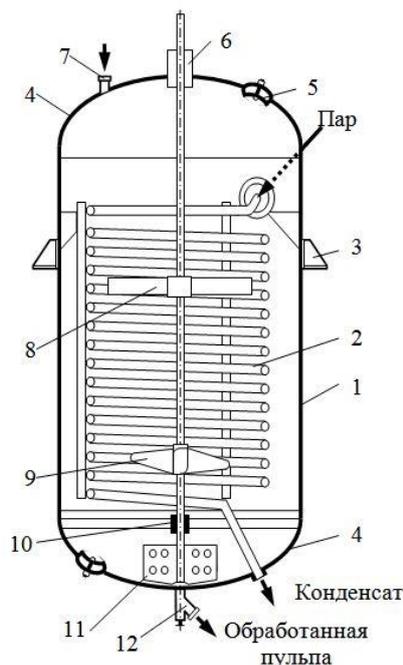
1 – корпус; 2 – змеевик; 3 – опора; 4 – сферические крышка и днище; 5 – люк; 6 – сальник; 7 – горловина; 8 – перемешивающее устройство лопастного типа; 9 – пропеллер; 10 – подшипник; 11 – перемешивающее устройство листового типа; 12 – разгрузочный вентиль
